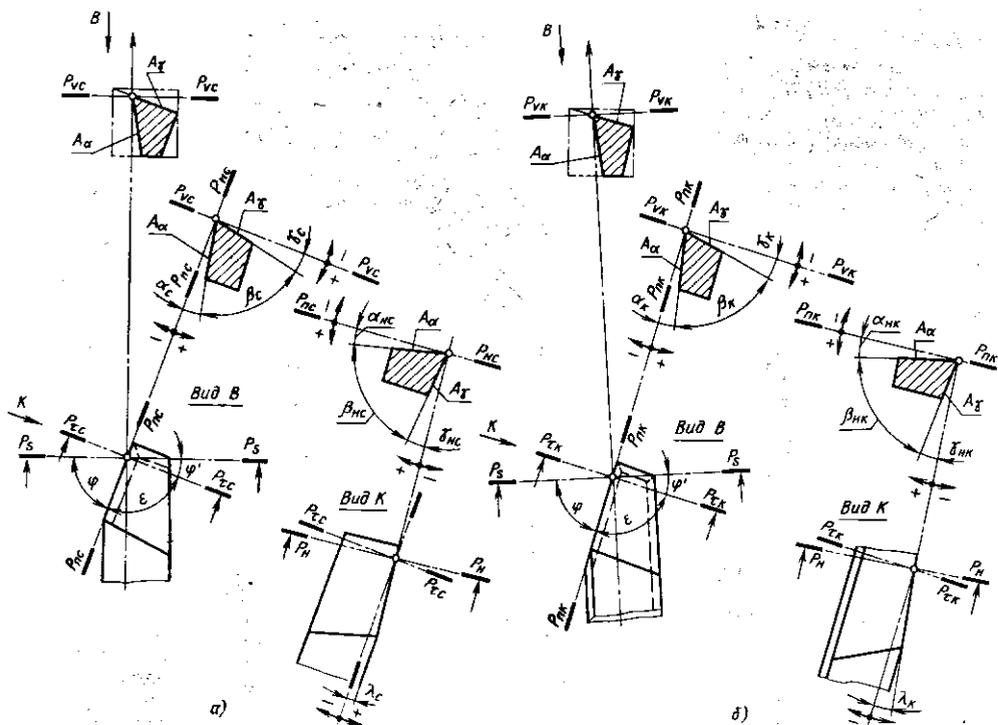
Углы токарного проходного реза системы координат: а — статической; б — кинематической
